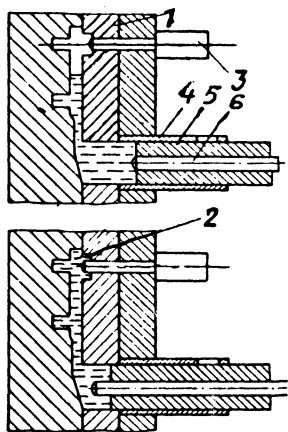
Схема процесса литья под давлением с подпрессовкой:
